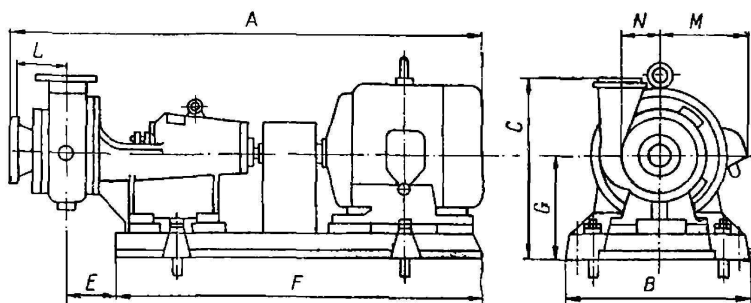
Общий вид и габаритные размеры насосов типа К (СД, Гр) с электродвигателями
